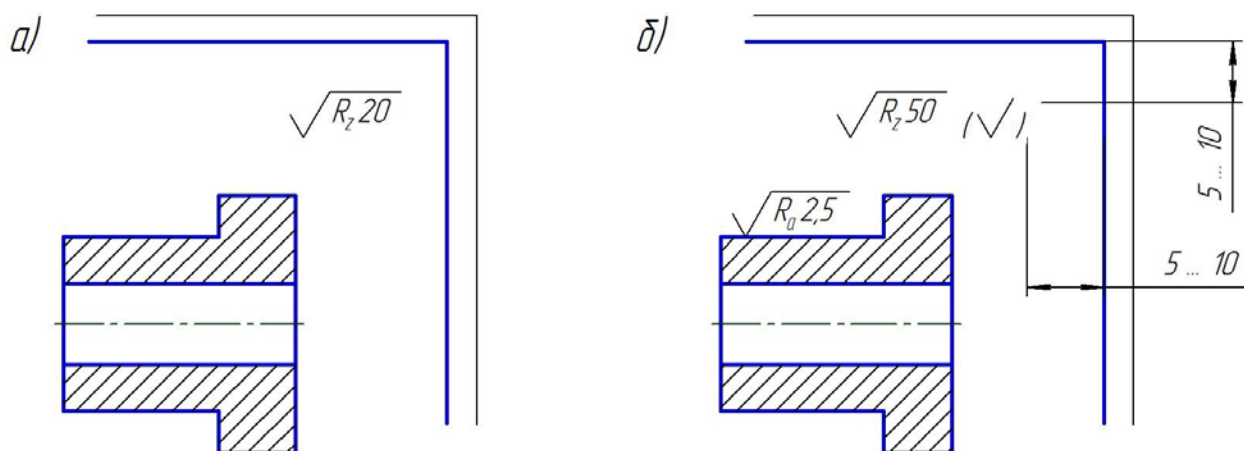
Примеры простановки на чертеже знака преобладающей шероховатости поверхности
